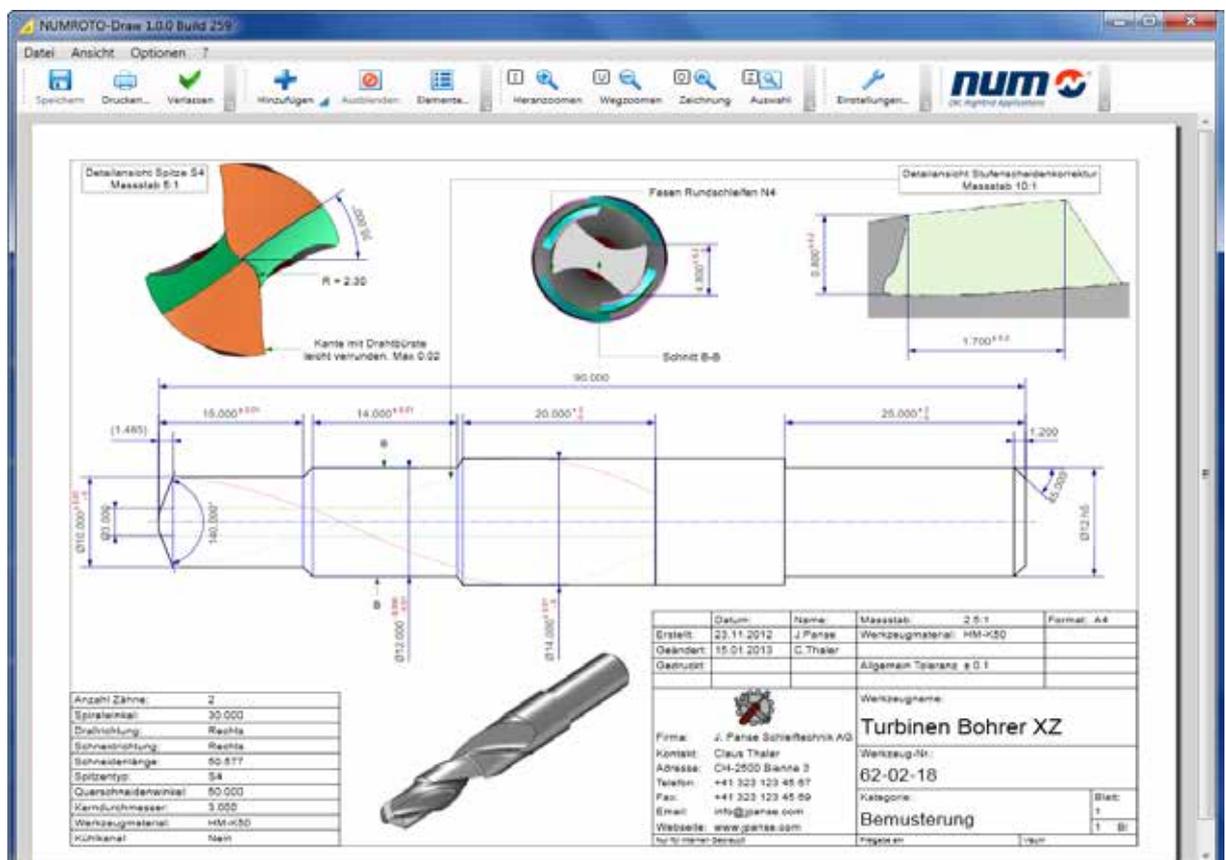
Werkzeugzeichnung eines Stufenbohrers erstellt mit NUMROTO Draw
